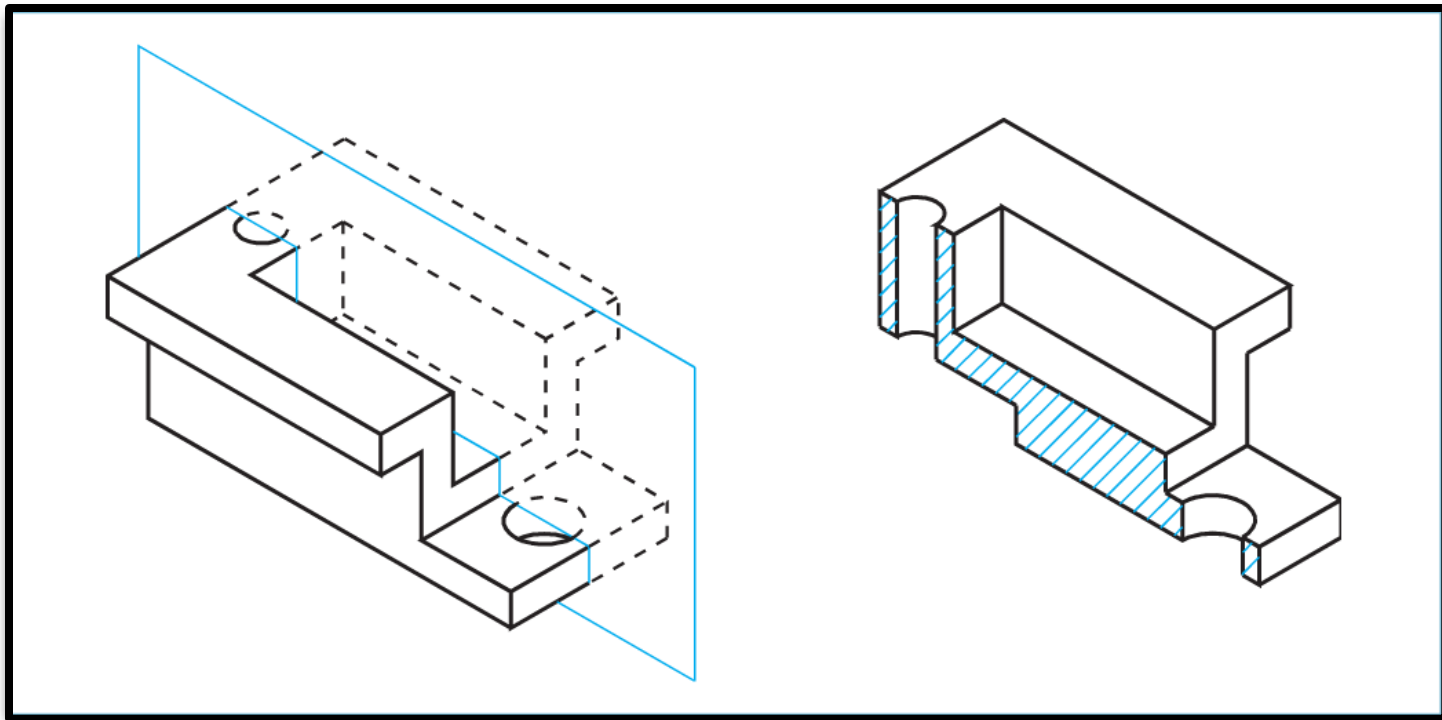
Sezionando con un piano longitudinale (piano di sezione) il pezzo di figura 1, viene facilitata la comprensione del pezzo
